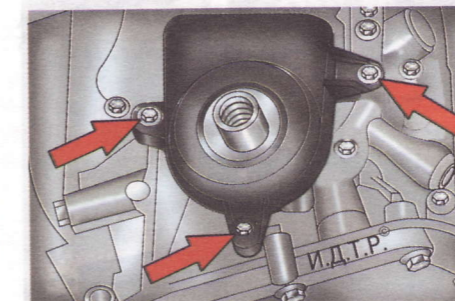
Нижняя крышка ремня привода газораспределительного механизма и ее крепление
